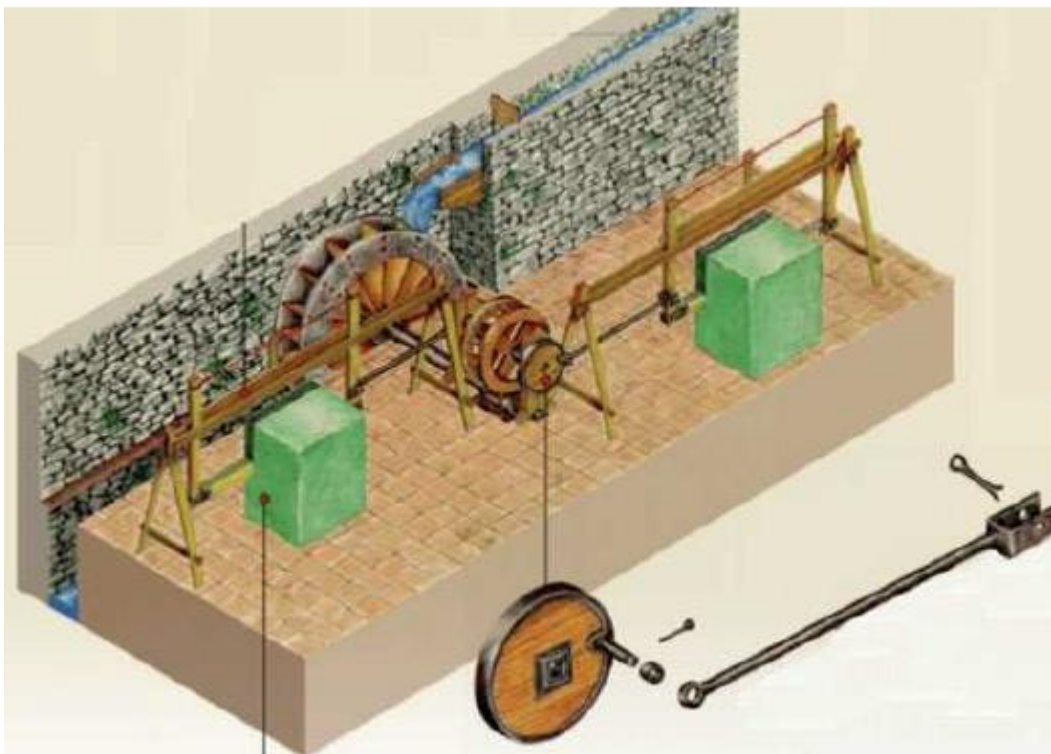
Disseny de la màquina de serrar de F. Russo i C.Rossi
